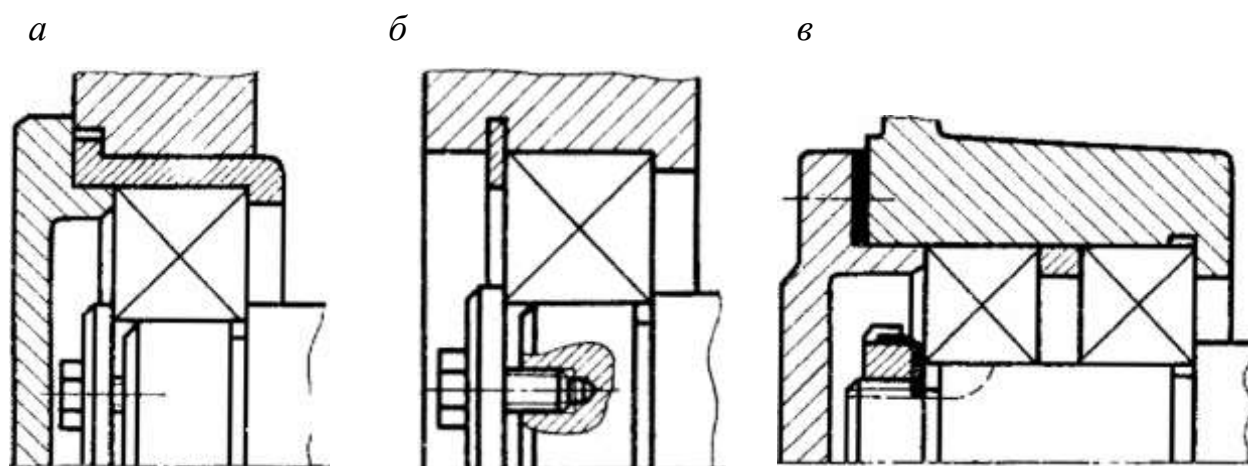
Способы закрепления наружных колец подшипников в корпусе:
